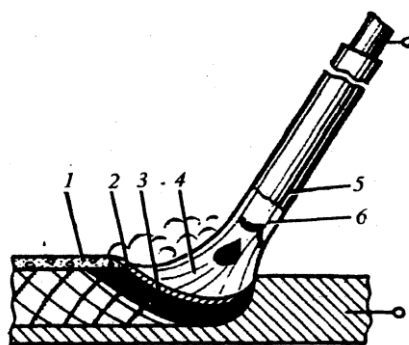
Схема дуговой электрической сварки металлическим электродом:
